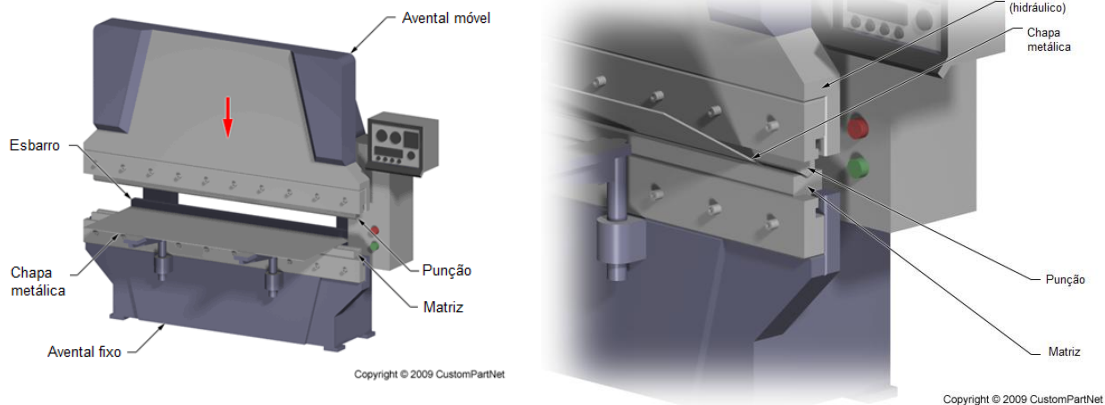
Elementos (à esquerda) e pormenor (à direita) de uma quinadora genérica (<http://www.custompartnet.com/wu/sheet-metal-forming>)
